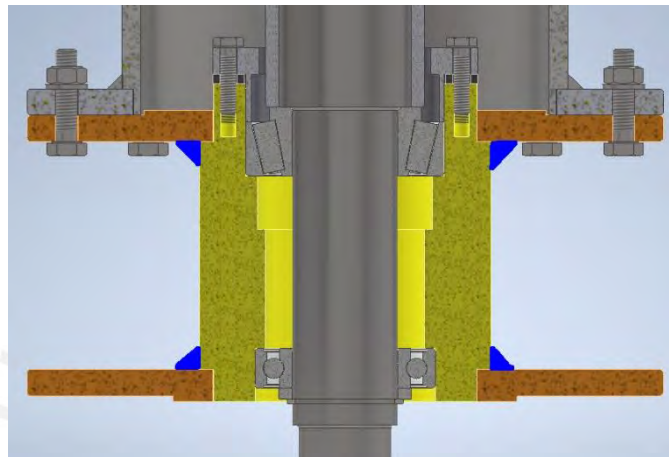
Soldadura entre la parte central y las caras del asiento de rodamientos.
